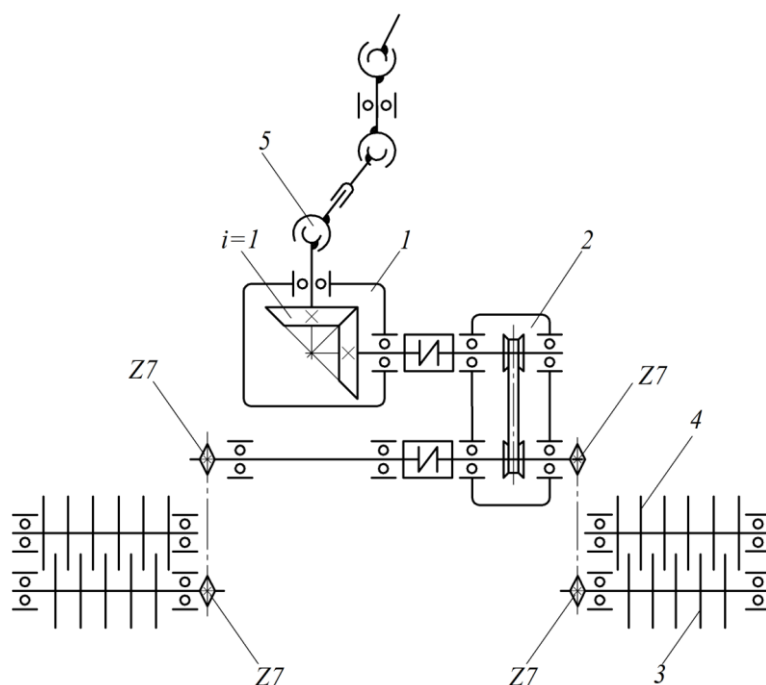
Кинематическая схема привода батареи активных зубчатых дисков
